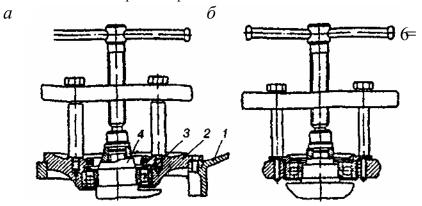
Выпрессовка кривошипного механизма или коленчатого вала универсальным съемником: а - выпрессовка кривошипного механизма; б - выпрессовка корпуса заднего подшипника; I - картер двигателя; 2 - корпус подшипника; 3 - шарикоподшипник; 4 - кривошипный механизм
